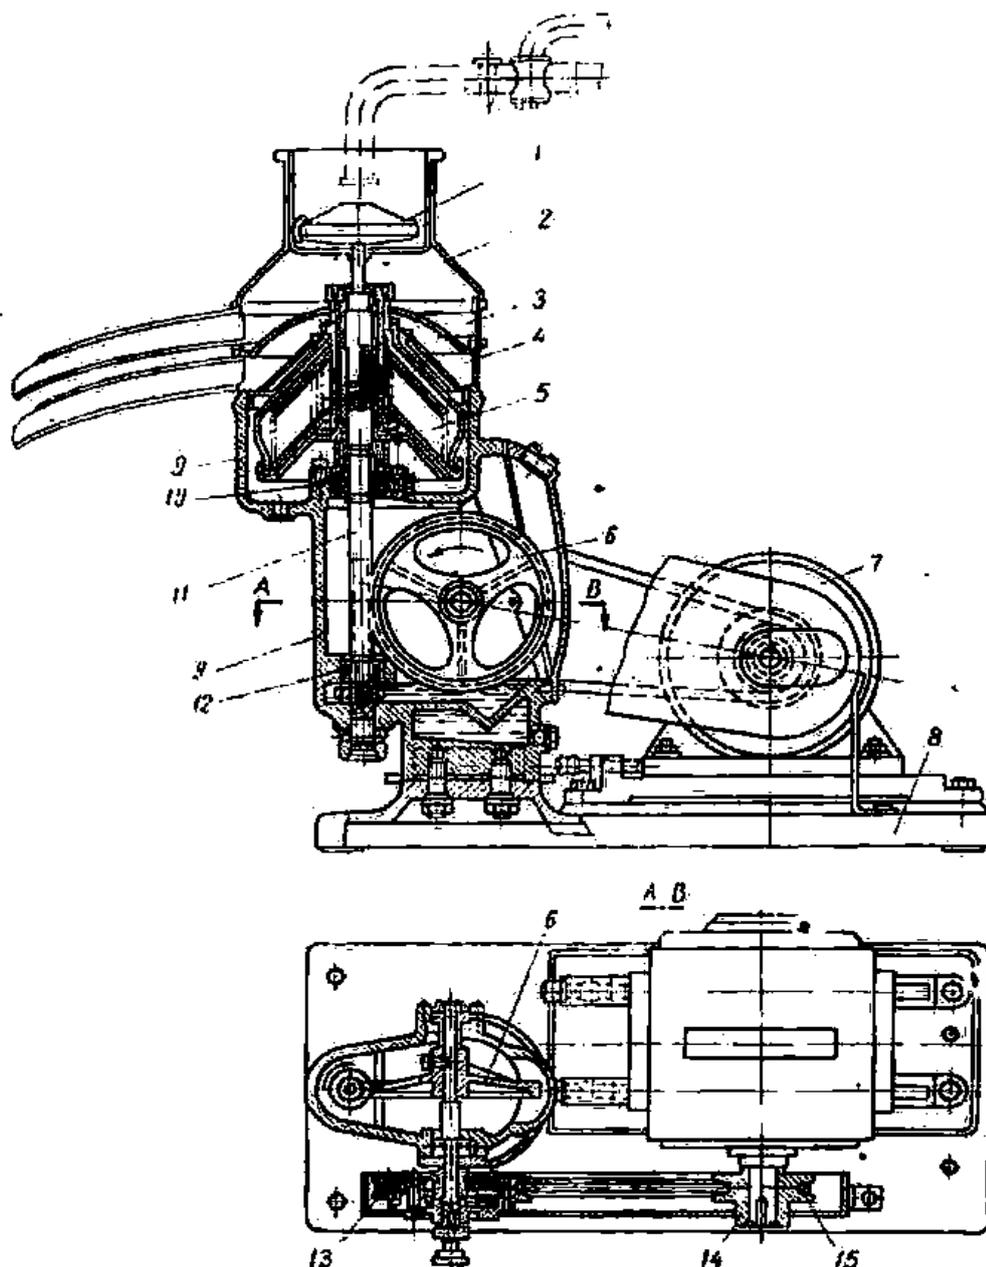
Открытый приводной сепаратор СМ-3-1000: 1 — поплавок; 2 — поплачковая камера; 3 — приемник сливок; 4 — приемник обезжиренного молока; 5 — барабан; 6 — винтовая шестерня; 7 — электродвигатель; 8 — плита; 9 — станина; 10 — горловой подшипник; 11 — веретено; 12 — упорный шарикоподшипник; 13 — шкив; 14 — шкив электродвигателя; 15 — клиновидный ремень
